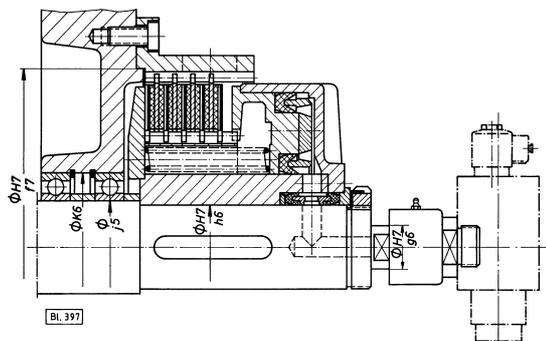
Pneumatisch betätigte Kupplung mit Flanschgehäuse;
